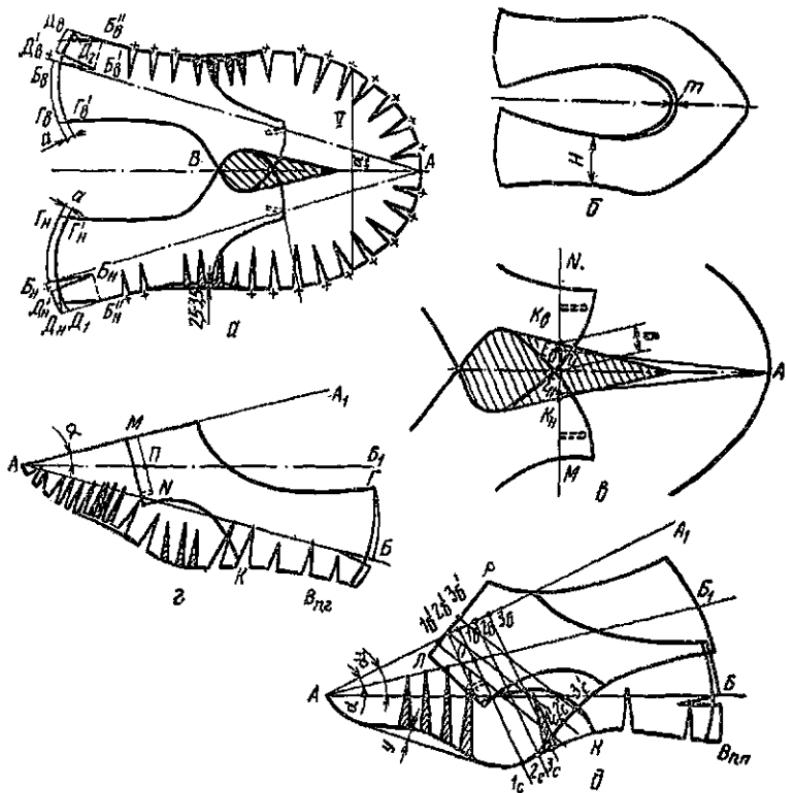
Схема получения условной развертки полуплоских и плоских заготовок верха обуви со свободной затяжной кромкой
